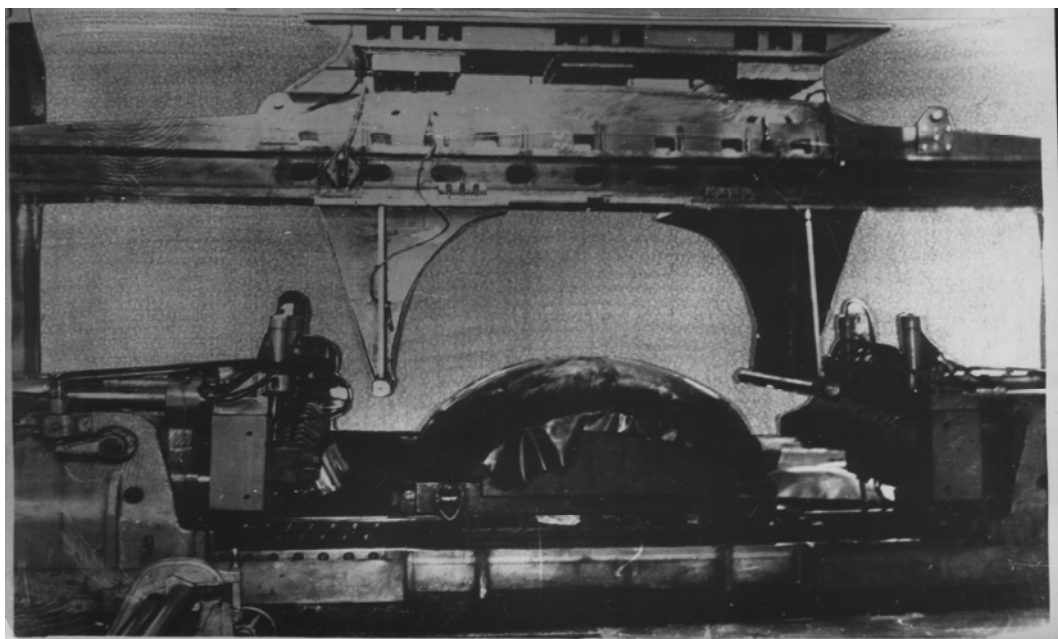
Обтяжной пресс РО-3М, приспособленный для формообразования обтяжкой элемента-осьмушки полусферической оболочки радиуса $R=5180$ мм при размерах заготовки $4000 \times 2100 \times 4,5$ (мм×мм×мм) из свариваемого алюминиевого сплава АМг6М
